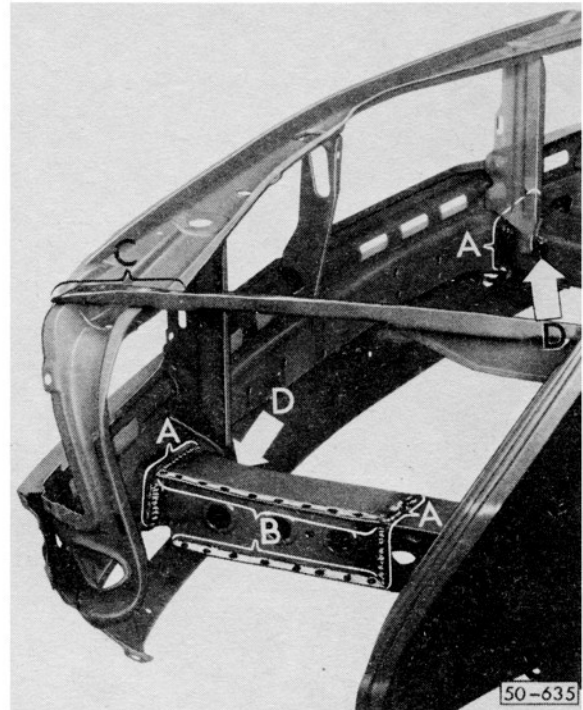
Abschlußblech vorn, Längsträger vorn innen Teilstück und Stegblech einschweißen.
